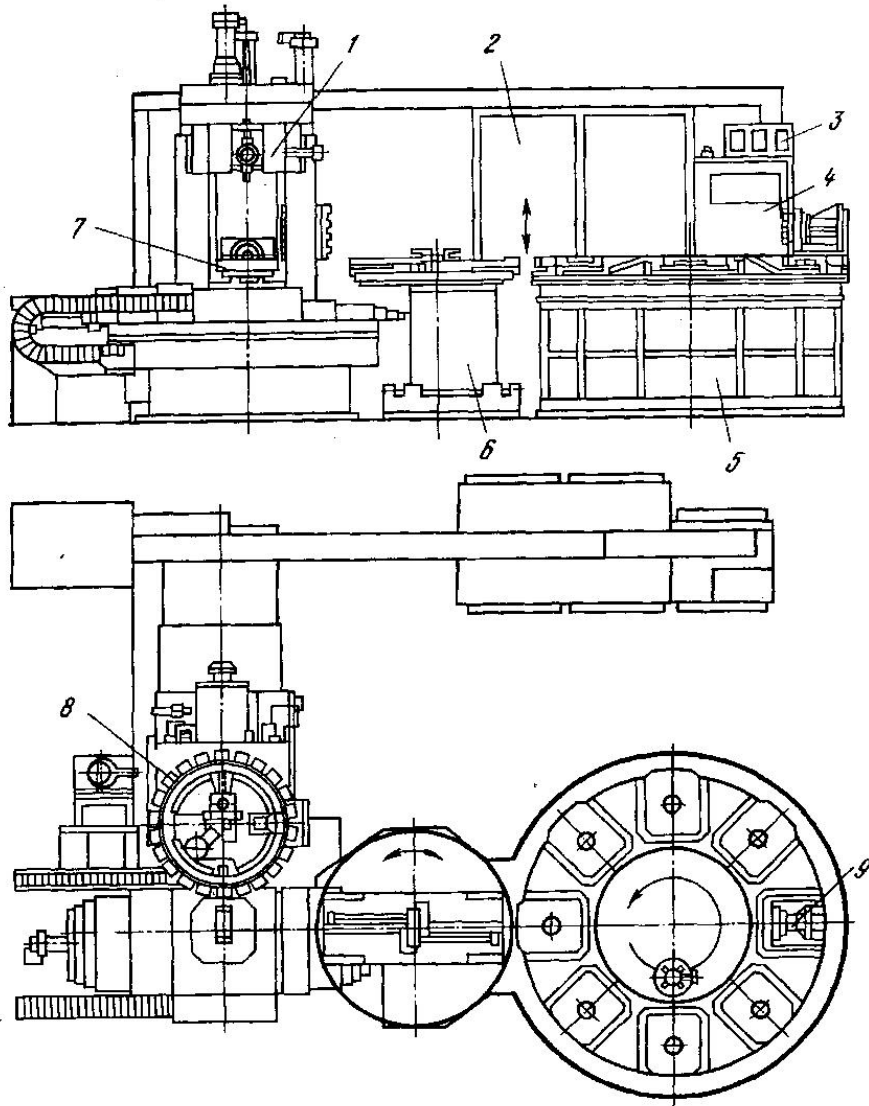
ГВМ для механічної обробки корпусних деталей: 1 – свердильно-фрезерно-розточний багатоцільовий верстат з ЧПК; 2 – електроустановка з ЧПК; 3 – контрольно-вимірювальна система; 4 – система ЧПК; 5 – накопичувач столів-супутників з оброблюваними деталями; 6 – пристрій для зміни столів-супутників; 7 – стіл-супутник; 8 – інструментальний магазин; 9 – пристрій заміни інструменту в магазині
